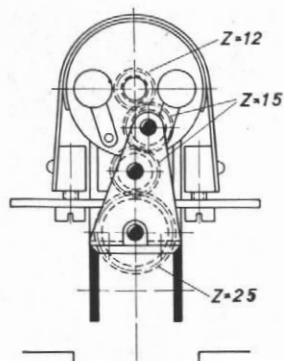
Schnitt durch Abb. 9 nach dem Schwungrad, Sichtrichtung Zahnradgetriebe und Motor.
